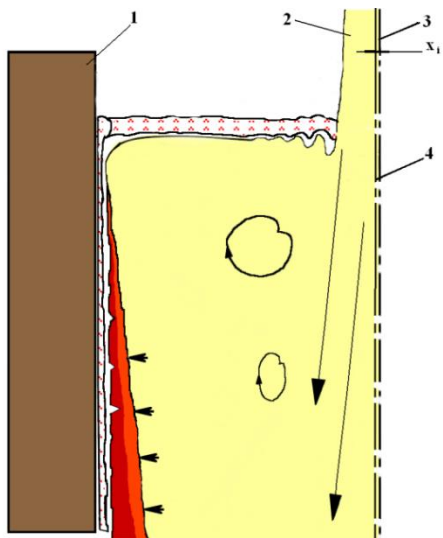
Размещения открытой струи металла в кристаллизаторе МНЛДЗ: 1 – широкая стенка кристаллизатора; 2 – поток металла; 3 – центральная ось кристаллизатора; 4 – ось потока металла из ковша; x_i – отклонения осей потока и кристаллизатора между собой
